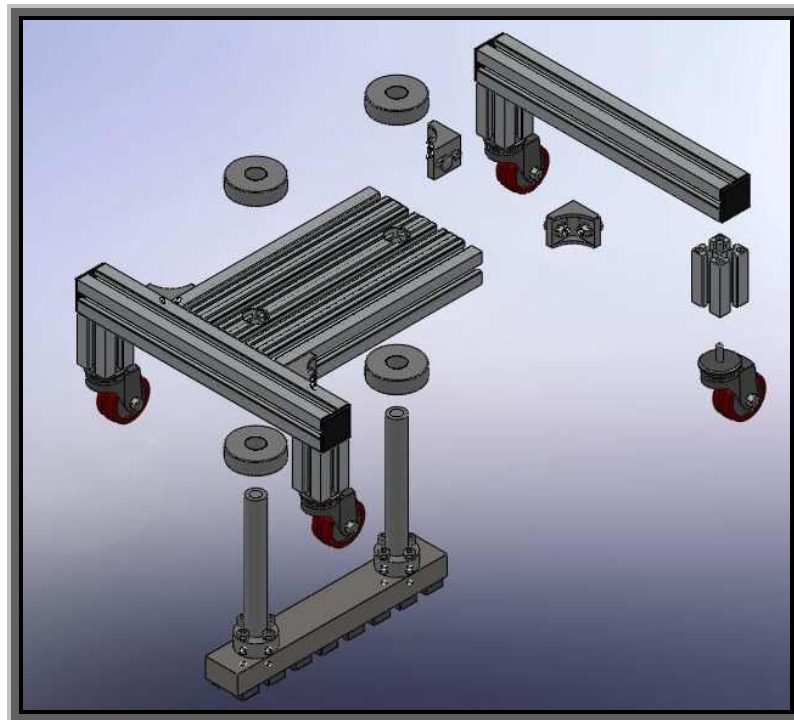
Vista frontal del conjunto final del MLSIP.
